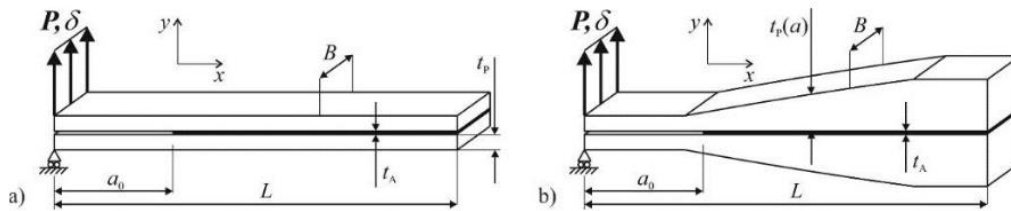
Provette DCB a) e provete TDCB b) de acordo com a norma ASTM D3433-99[39].
